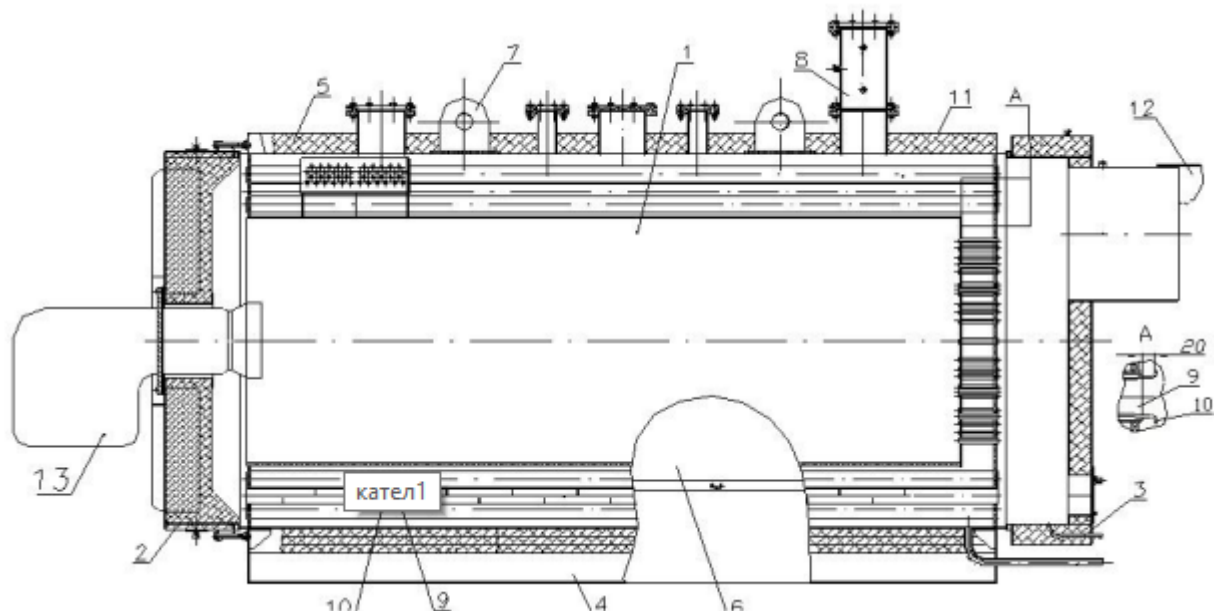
Пристрій котла КВ-1,86Г 1-корпус; 2-дверцята топки; 3-короб димових газів; 4-опора; 5-теплоізоляція; 6-облицювання; 7-стропова сережка;
